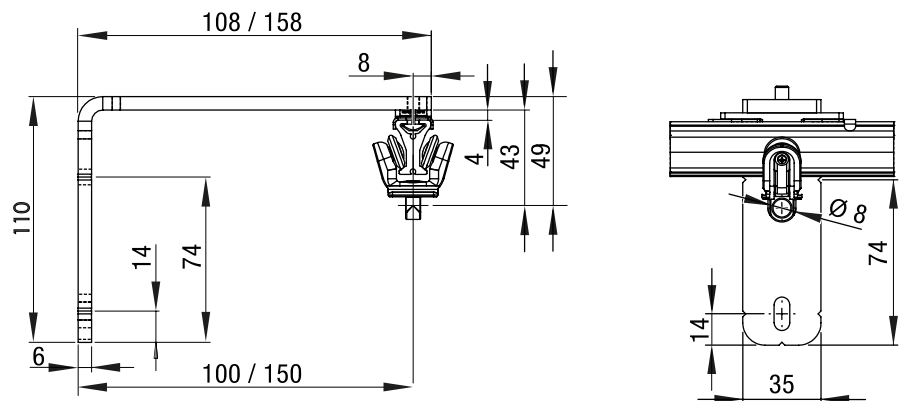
Interior-Wandarm mit Deckenmontageplatte – Einbaumaße
